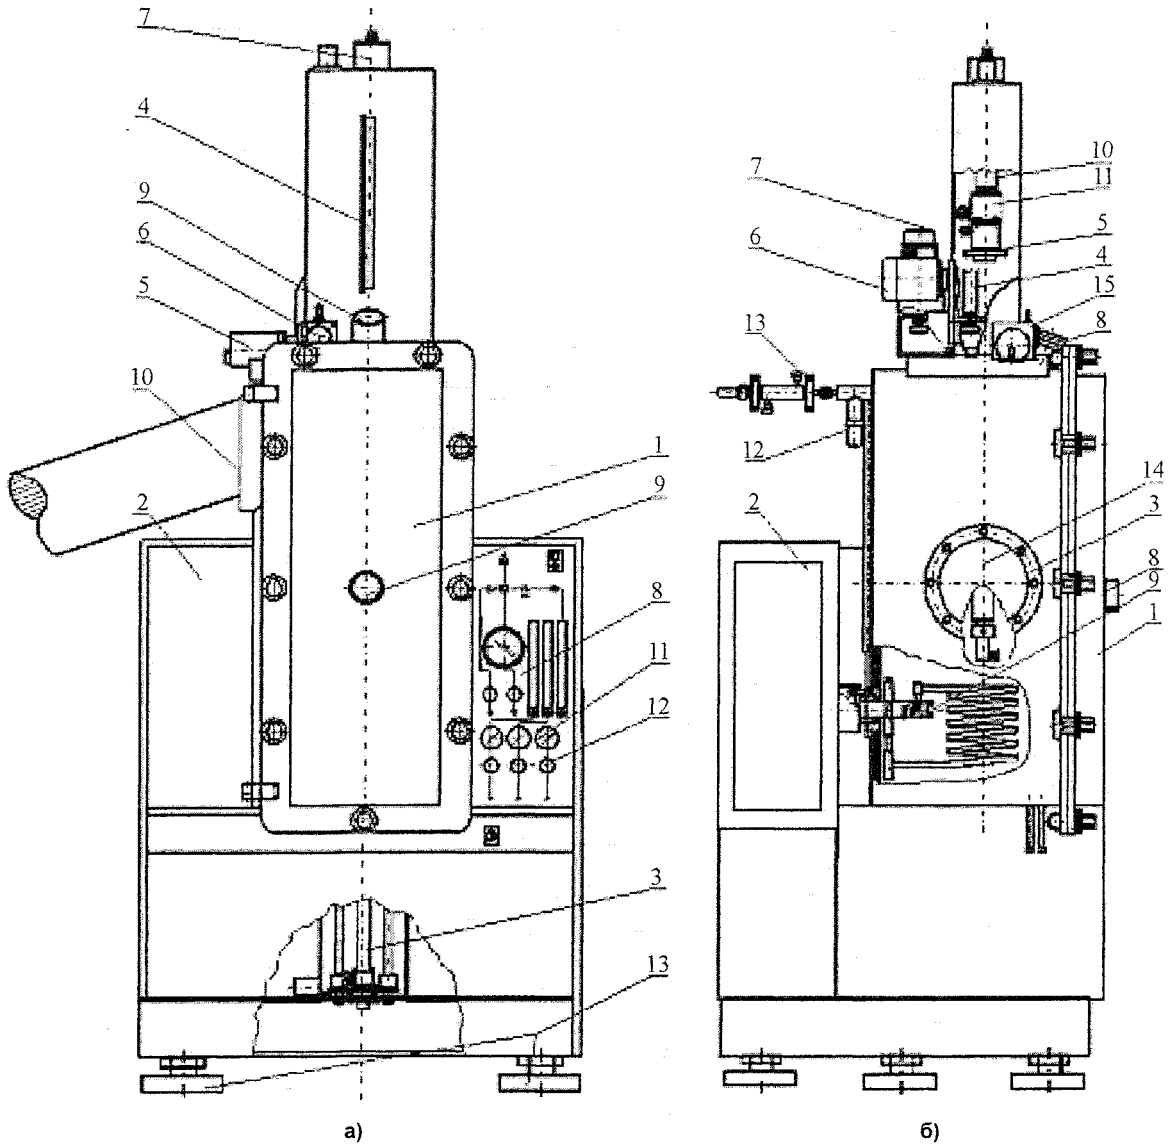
Установка «Кристалл 3М»: а – фронтальный вид; б – вид сбоку.
